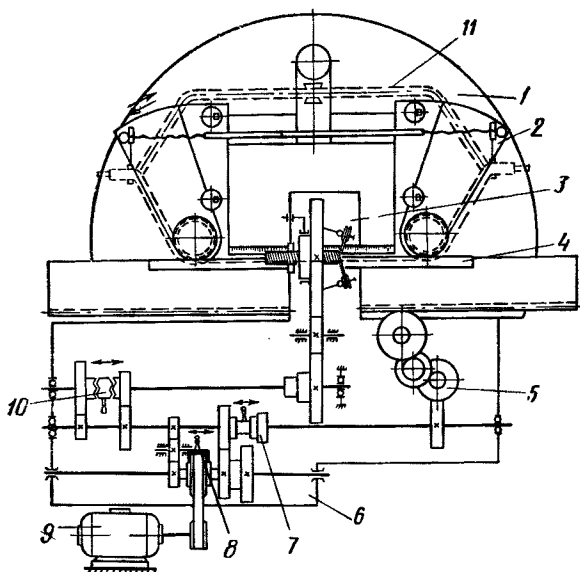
Кинематическая схема изолировочного станка ЛШ-4
